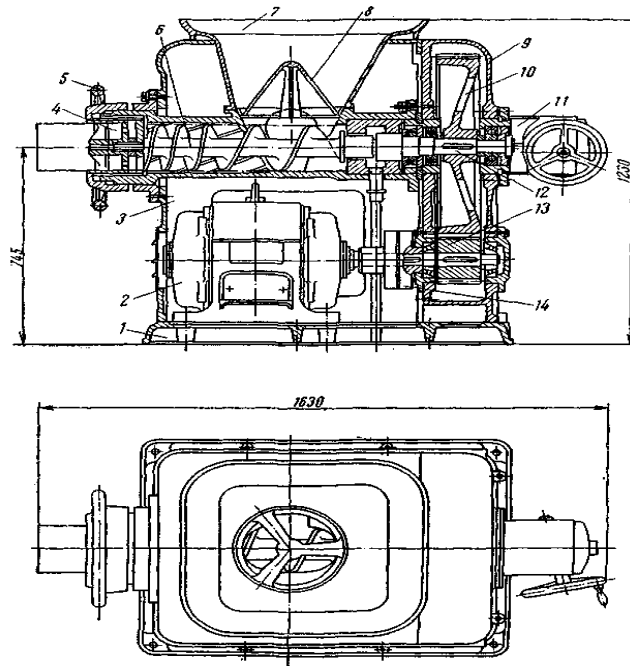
Вовчок МП-2-220: 1 – плита; 2 – електродвигун; 3 – станина; 4 – комплект ріжучого механізму; 5 – гайка-маховик; 6 – робочий циліндр; 7 – приймальна чаша; 8 – запобіжник; 9 – корпус редуктора; 10 – зубчасте колесо; 11 – механізм виштовхувача робочого шнека; 12 – трансмісійний вал; 13 – шестерня; 14 - пружна втулочно-пальцева муфта.
